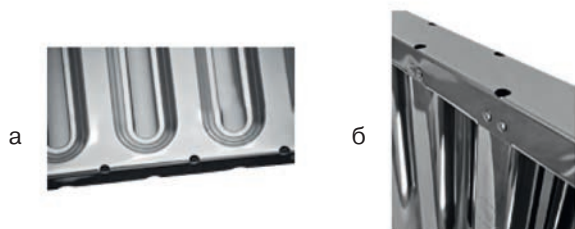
Экранные (лабиринтные) механические фильтры: а – сварная конструкция; б – сборная конструкция
